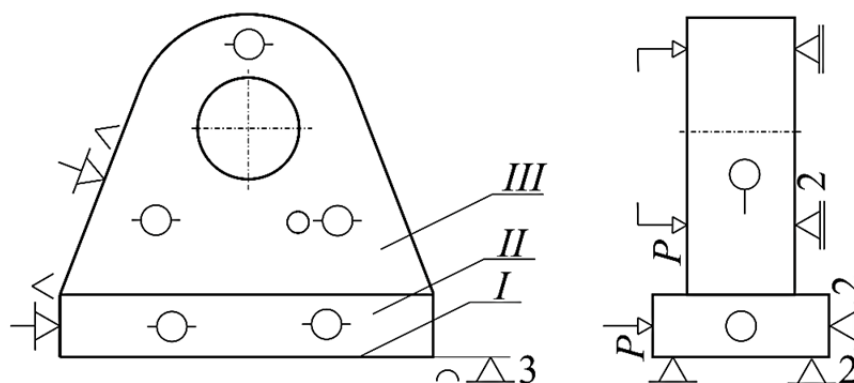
Принципиальная схема приспособления для сборки проушины
